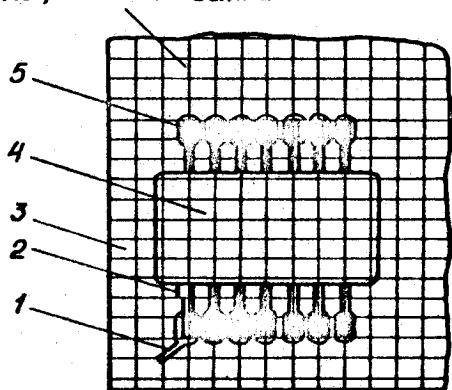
Розміщення корпусних мікросхем з планарними виводами на печатній платі зі стандартною координатною сіткою: 1 – ключ; 2- перший вивід корпусу IC; 3 – печатна плата; 4 – корпус IC; 5 – контактна площадка
